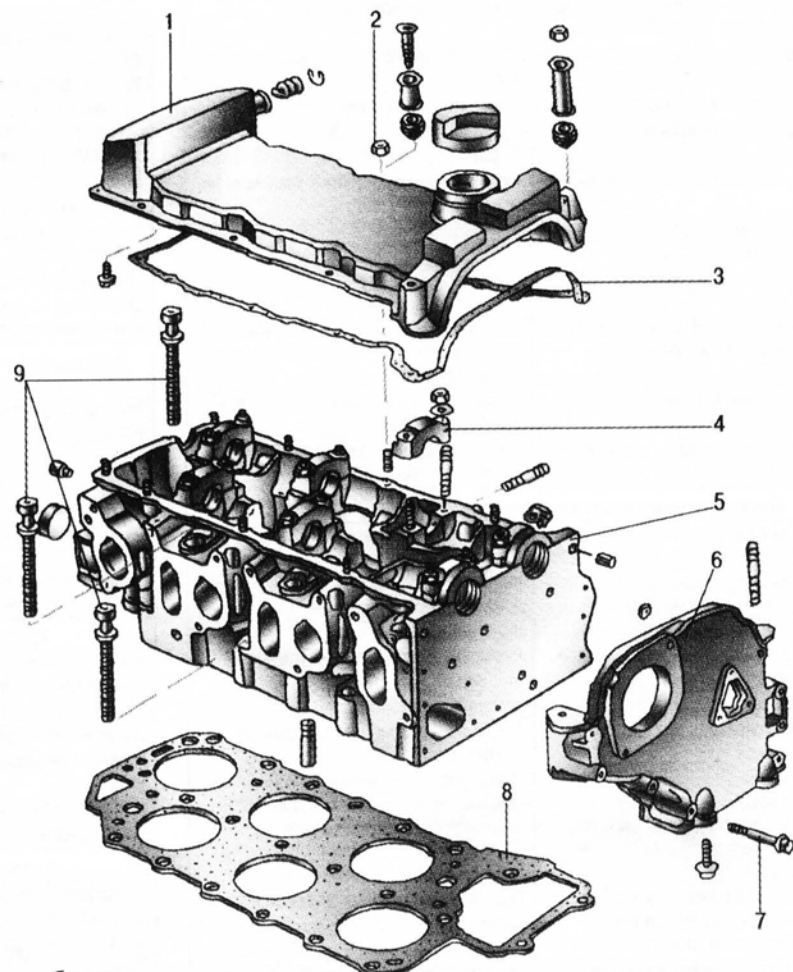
Головка блока цилиндров двигателя ААА: 1 — крышка головки блока цилиндров; 2 — гайка крепления крышки головки блока цилиндров; 3 — прокладка крышки головки блока цилиндров; 4 — крышка подшипника распределительного вала; 5 — головка блока цилиндров; 6 — крышка привода ГРМ; 7 — болт крепления крышки ГРМ; 8 — прокладка головки блока цилиндров; 9 — болты крепления головки блока цилиндров
